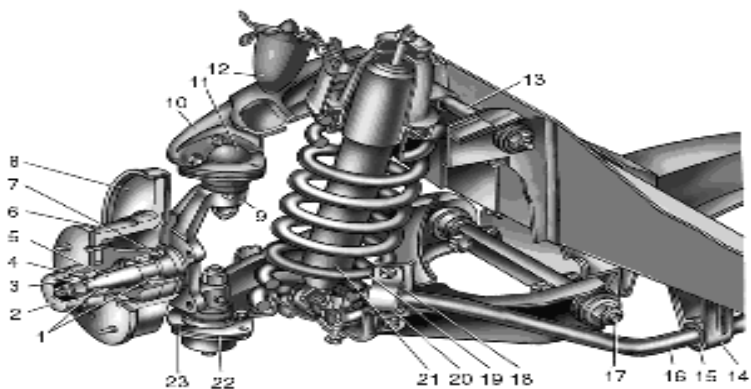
Передняя подвеска, на примере автомобиля ВАЗ 2105 1 - подшипники ступицы переднего колеса; 2 - колпак ступицы; 3 - регулировочная гайка; 4 - шайба; 5 - цапфа поворотного пальца; 6 - ступица колеса; 7 - сальник; 8 - тормозной диск; 9 - поворотный кулак; 10 - верхний рычаг подвески; 11 - корпус подшипника верхней опоры; 12 - буфер хода сжатия; 13 - ось верхнего рычага подвески; 14 - кронштейн крепления штанги стабилизатора; 15 - подушка штанги стабилизатора; 16 - штанга стабилизатора; 17 - ось нижнего рычага; 18 - подушка штанги стабилизатора; 19 - пружина подвески; 20 - обойма крепления штанги амортизатора; 21 - амортизатор; 22 - корпус подшипника нижней опоры; 23 - нижний рычаг подвески
